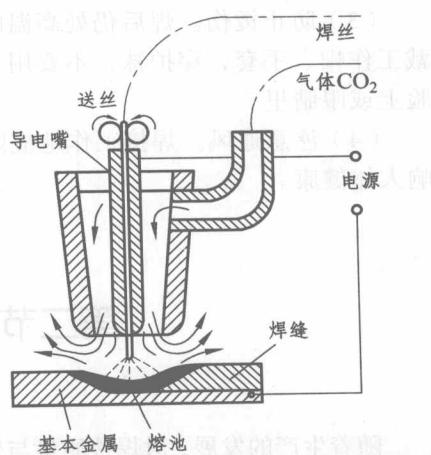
二氧化碳气体保护焊的工作原理
